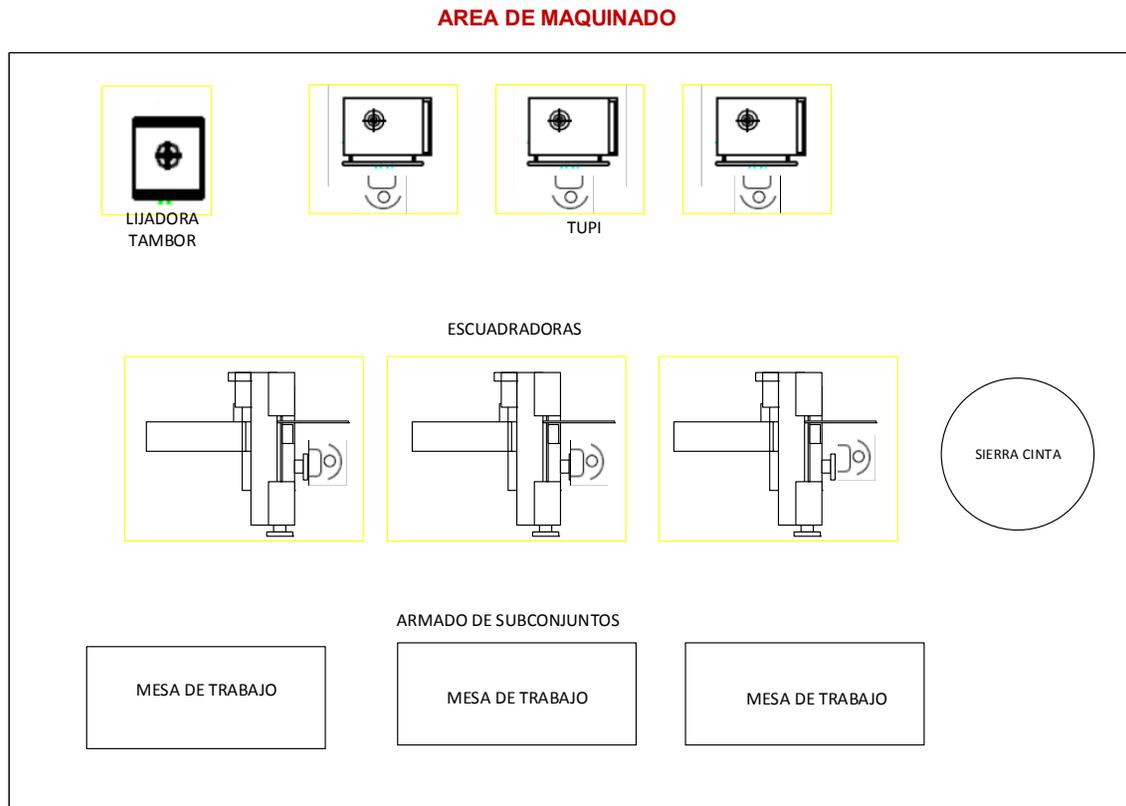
LAYOUT DEL AREA DE MAQUINADO
